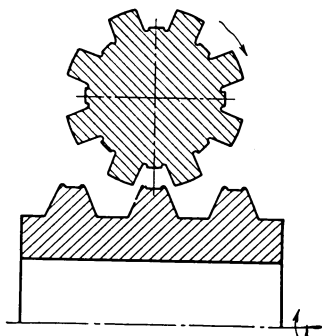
Схема фрезерования зубьев вала червячной фрезой
